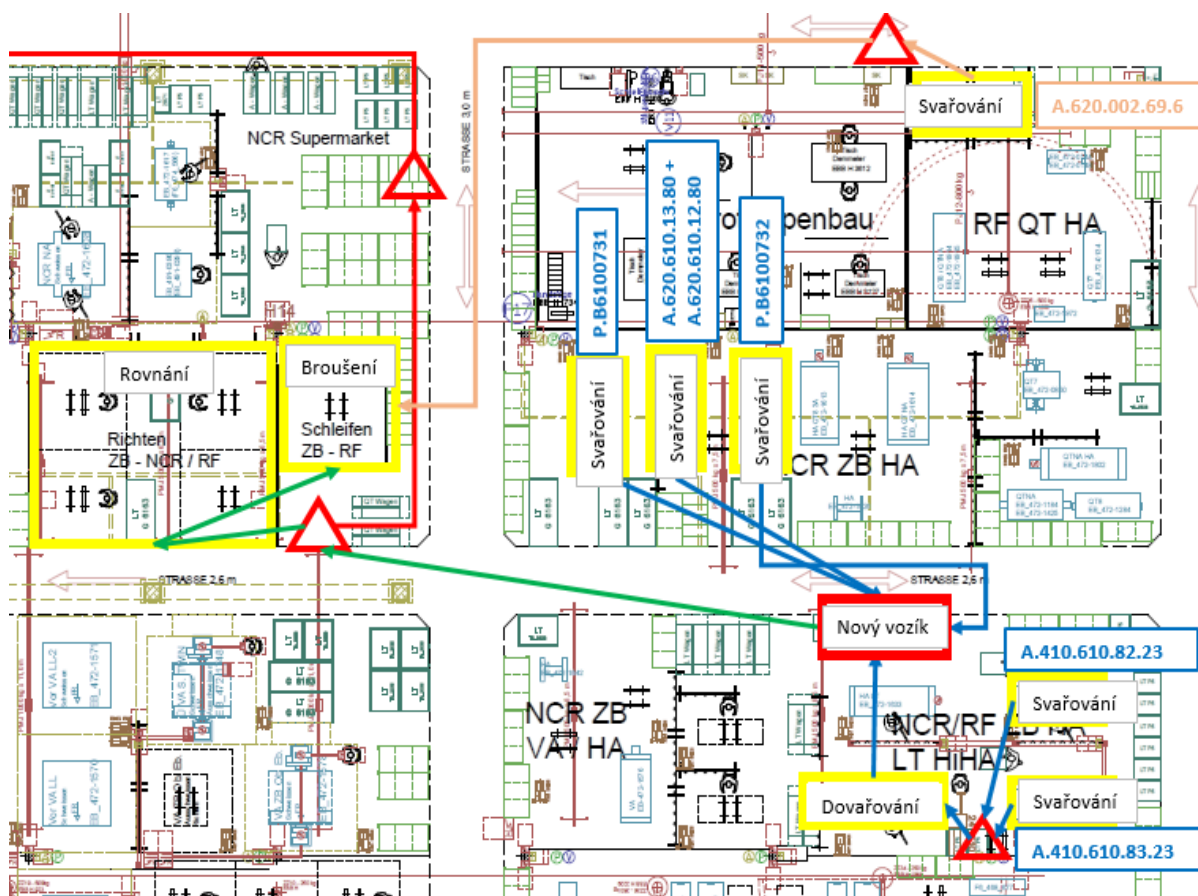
Standardizované místo uložení vozíku I.
